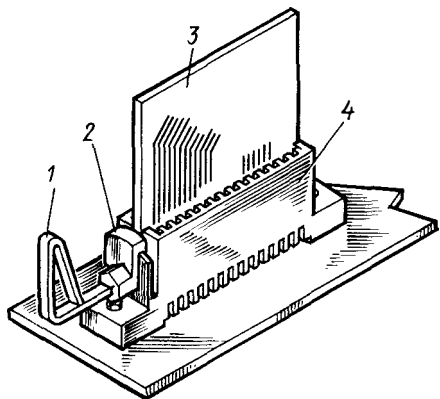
Соединитель с нулевым усилием сочленения для печатной платы: 1—кулачковый ключ; 2—замок; 3—печатная плата; 4—розетка соединителя
